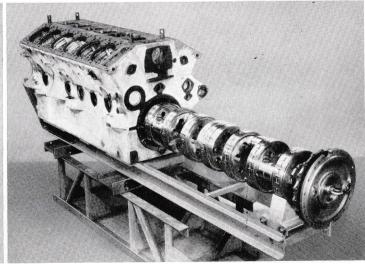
Posición de partida al montar el eje cigüeñal en el cárter del motor de la fig. 2
